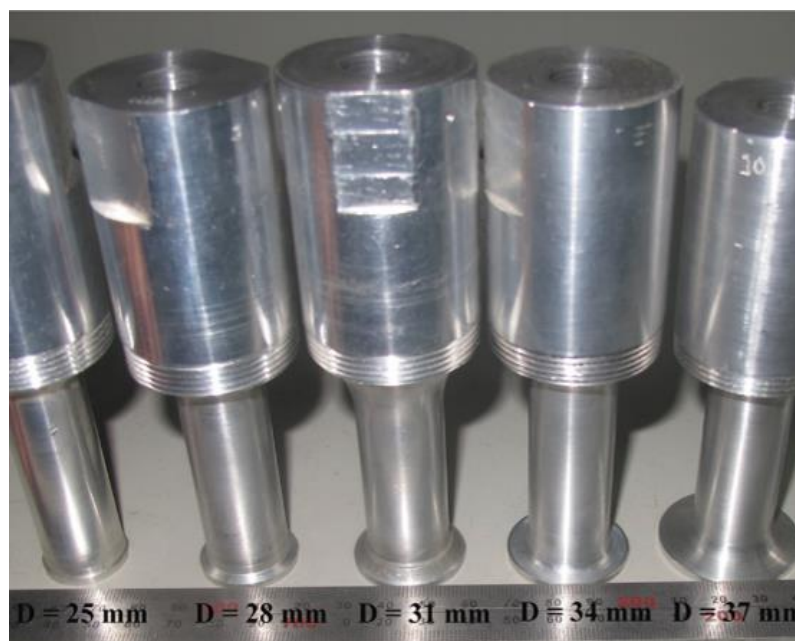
Концентраторы ультразвуковых колебаний с различными диаметрами излучателей [47]
